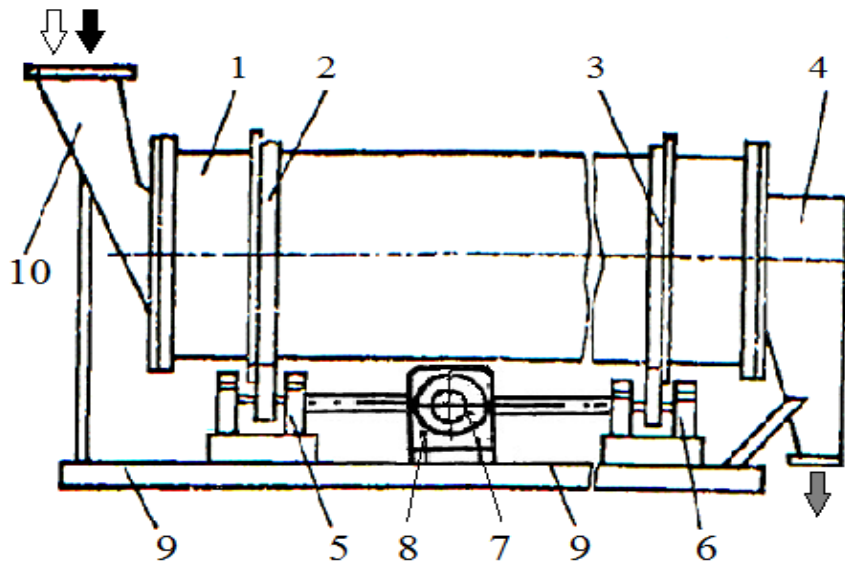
Смеситель с гладким цилиндрическим корпусом
